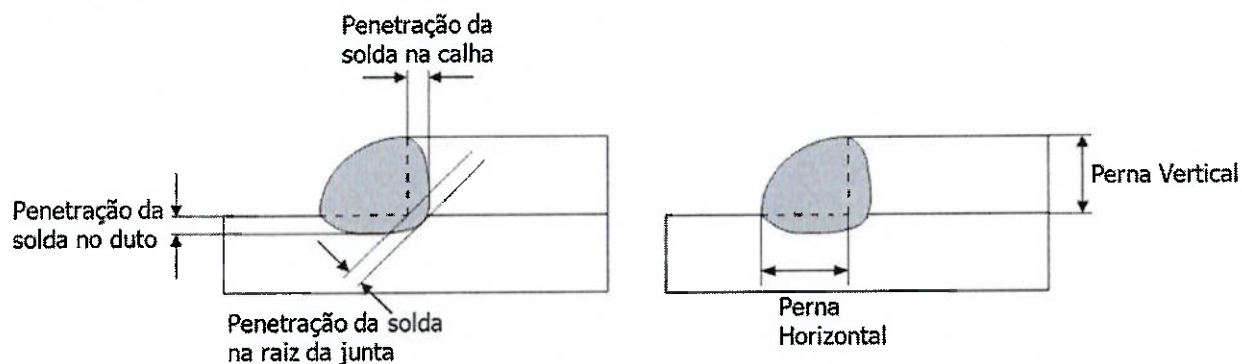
Dimensional da solda para os ensaios de macrografia.
